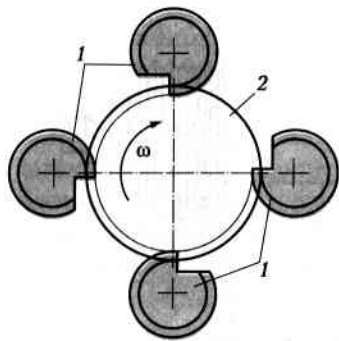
Схема нарезания метрической резьбы резьбонарезной головкой с круглыми гребенчатыми плашками
